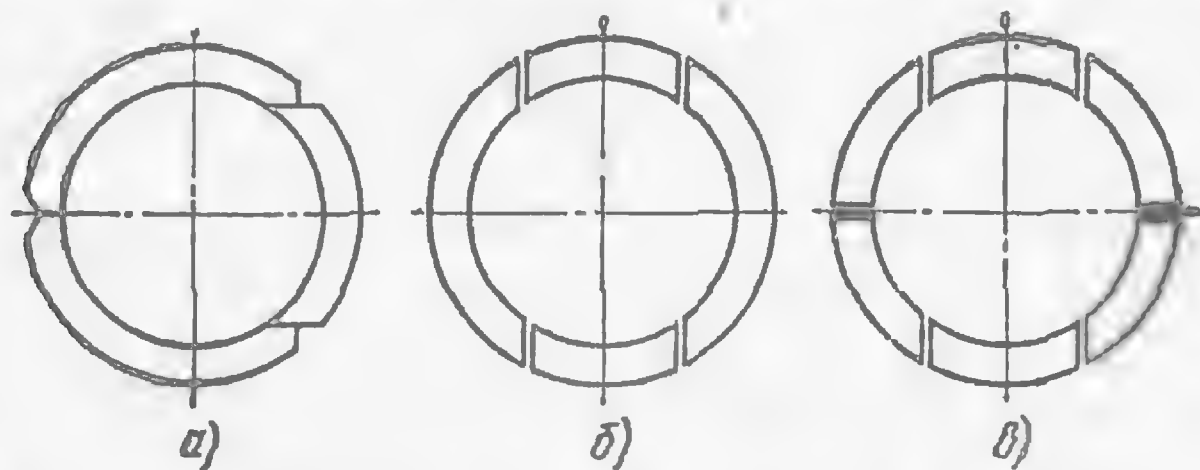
Конструкции опорных элементов в самоуплотняющихся соединениях крышки с корпусом
